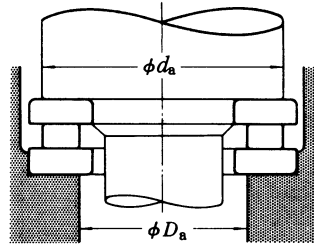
Diâmetro da Superfície de Suporte do Rolamento Axial de Rolos
